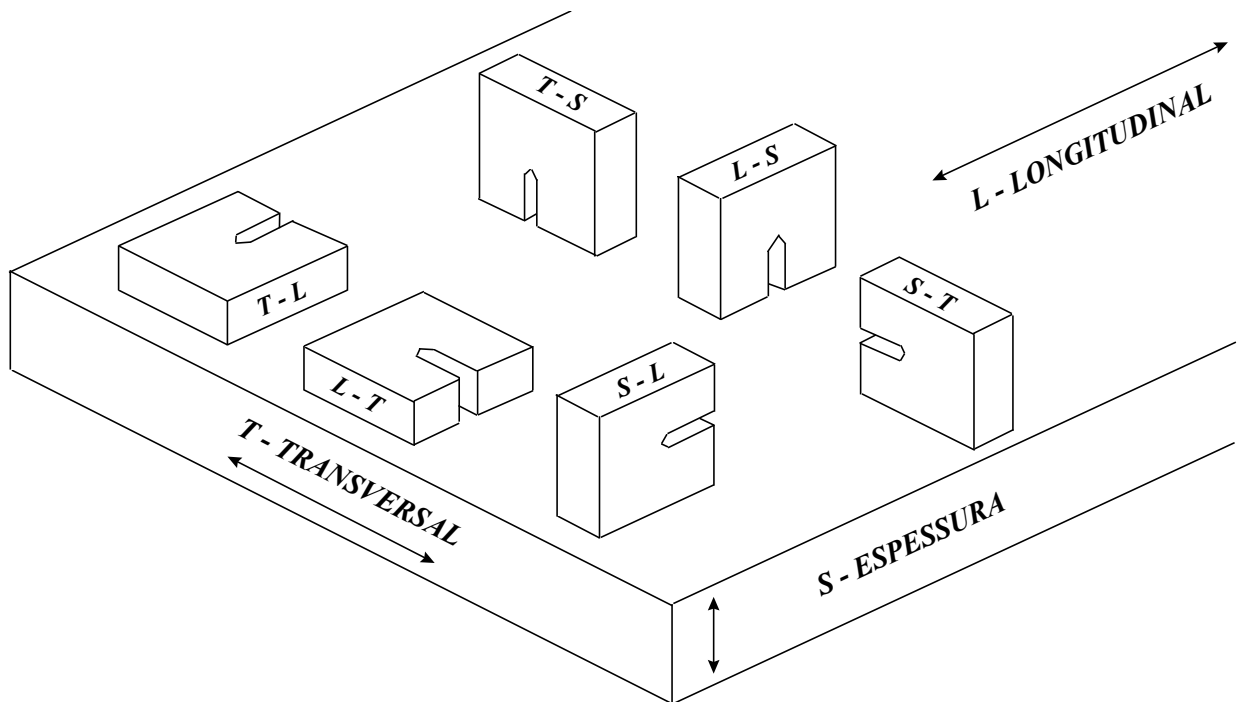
Forma de retirada e nomenclatura de corpos de prova na forma de chapa [ASTM E399-91].
